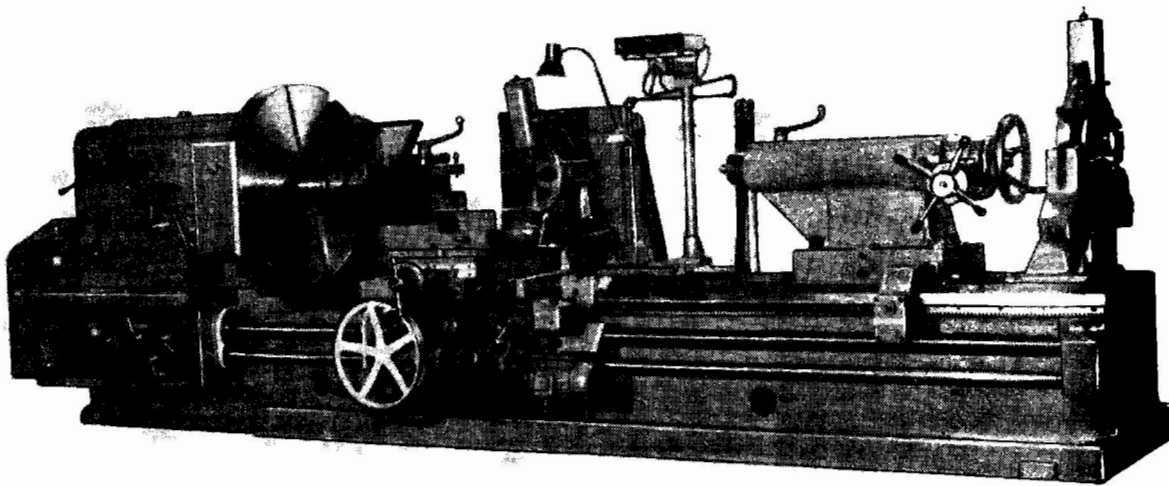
Общий вид станка мод. 1H65.Ф1
